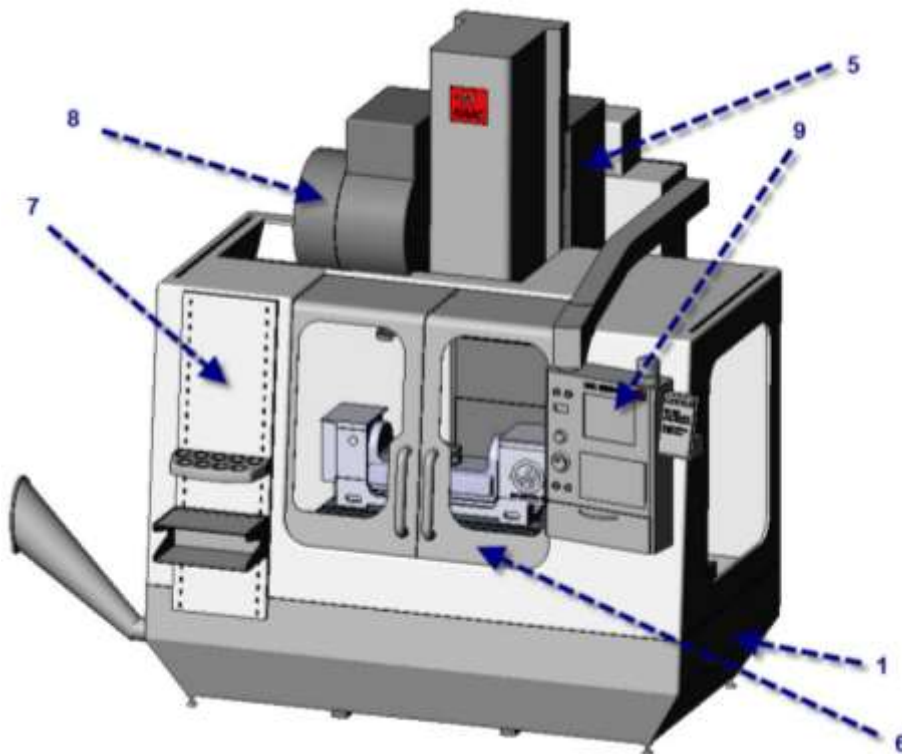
Корпус вертикально-фрезерного верстата з ЧПУ
